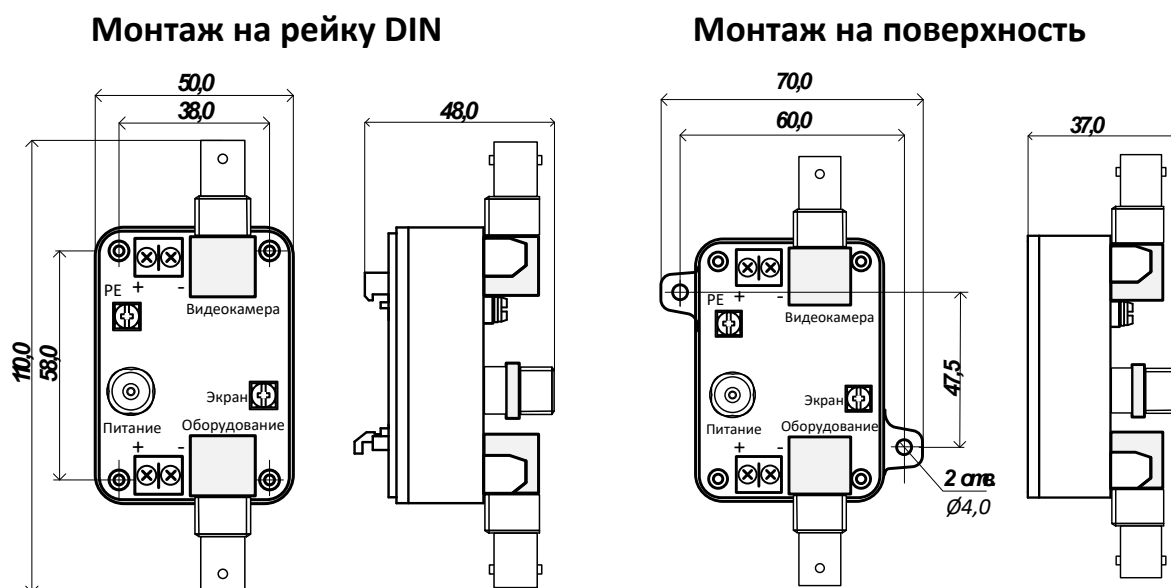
Габаритные и установочные размеры устройства УПК
